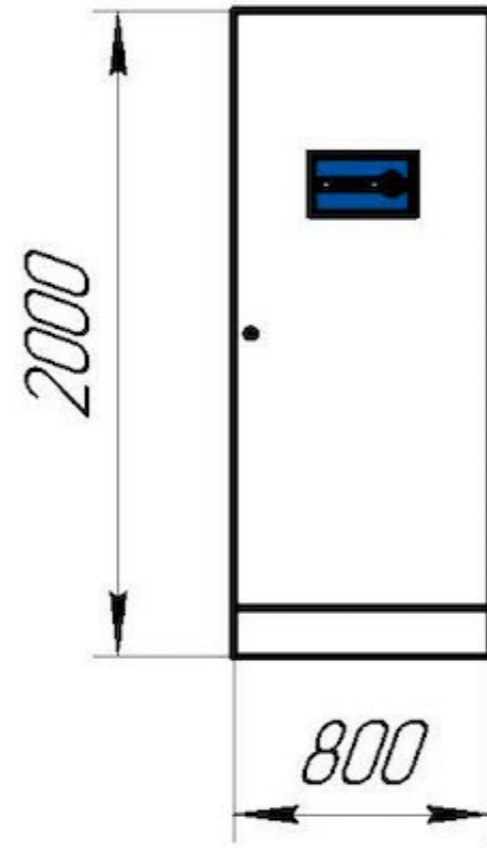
Габаритный чертеж устройства автоматического ввода резерва
